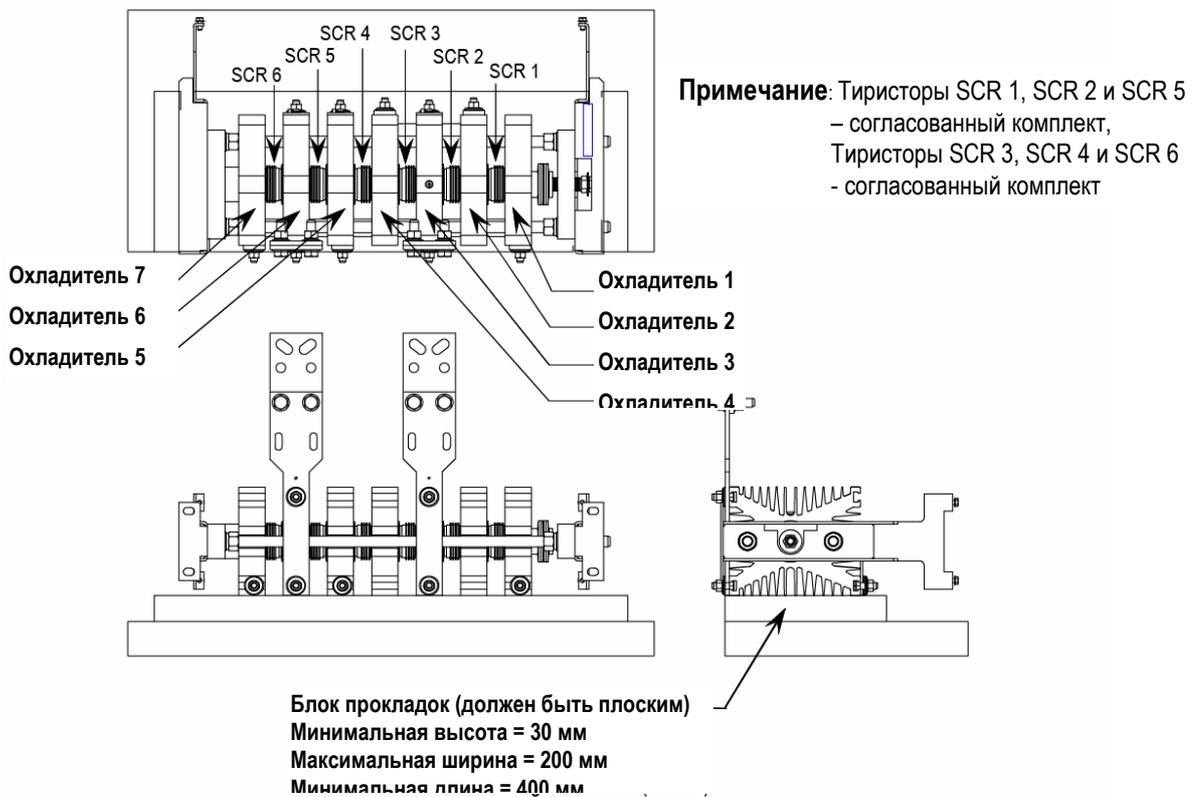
Сборка охладителя 6900 В, 180 / 360 А
